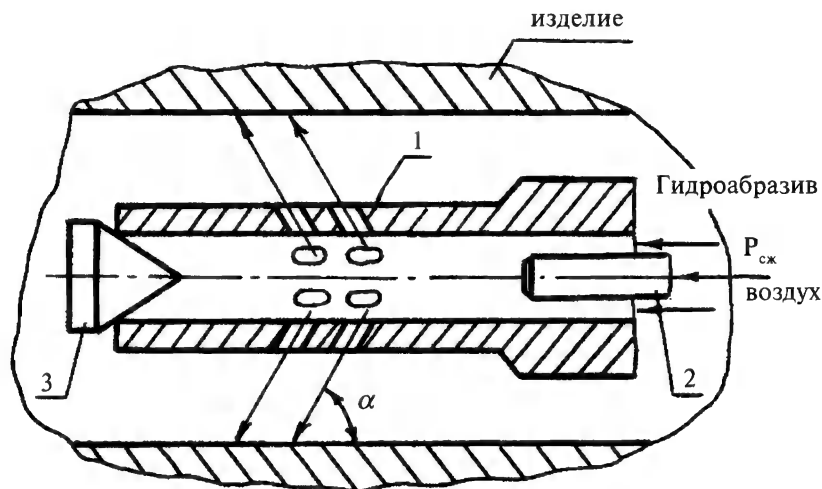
Схема гидрополирования форсуночной головкой: 1 - корпус, 2 - форсунка, 3 - пробка
